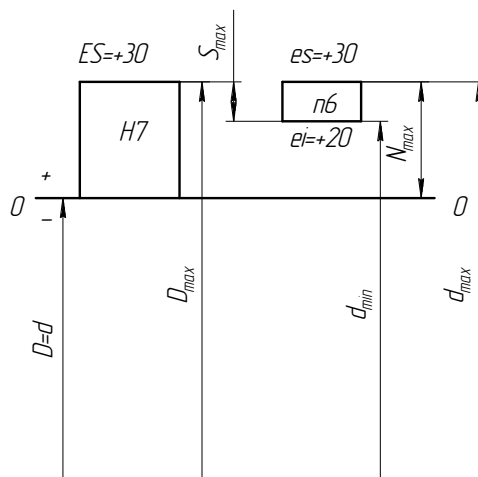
Схема расположения полей допусков посадки $\varnothing 65 \frac{H7}{n6}$
